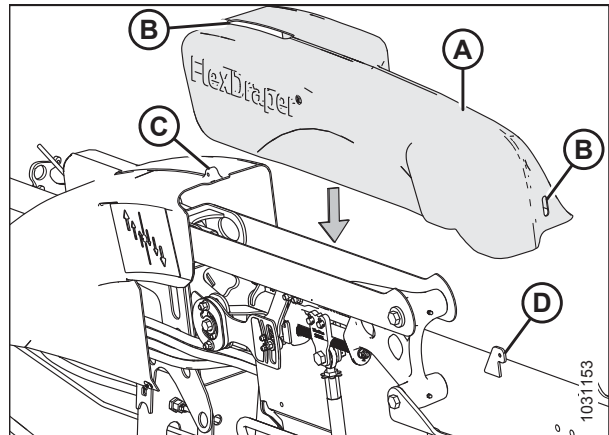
Cubierta de conexión de flexión: lado izquierdo
